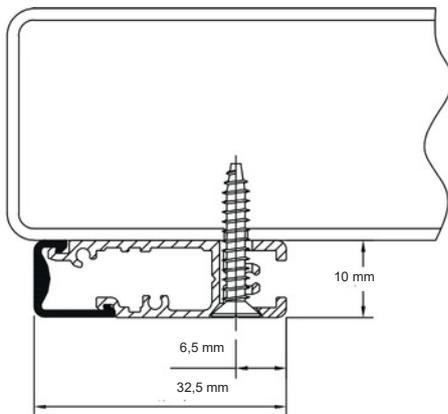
Profilo fisso da 10 mm con vite autofilettante a testa svasata
